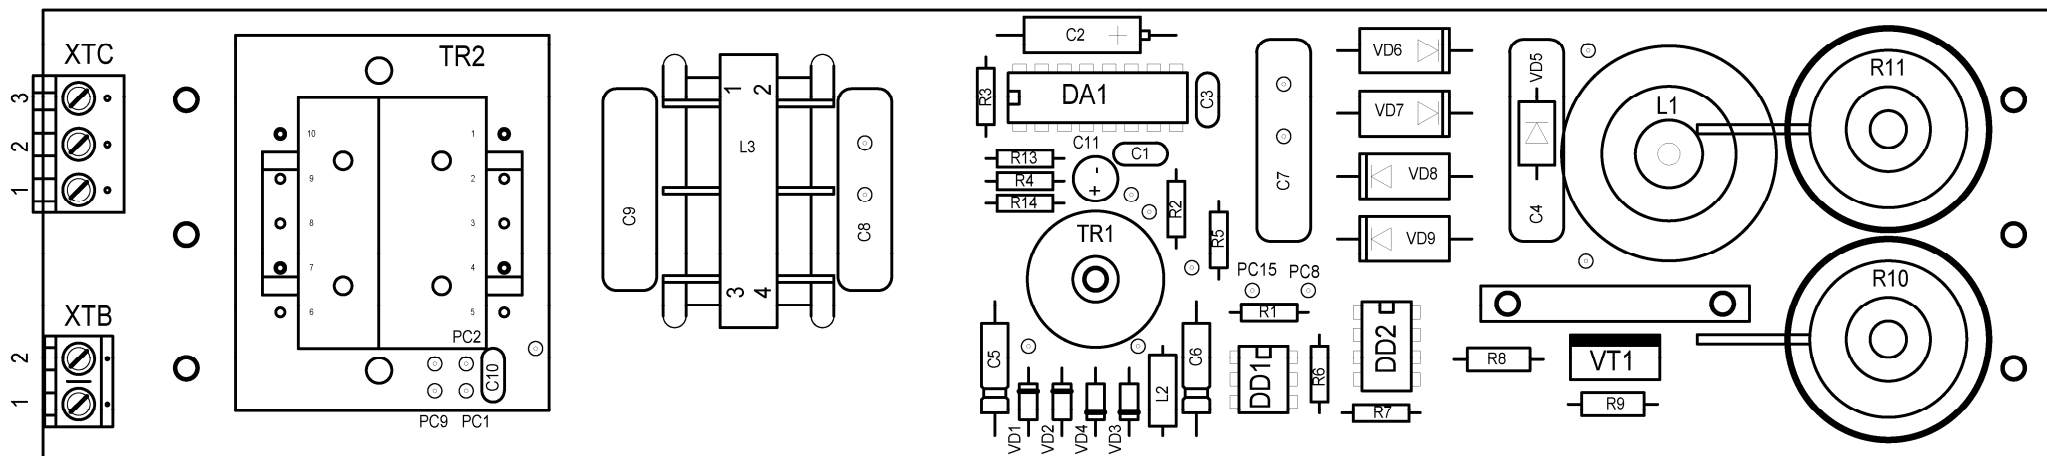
Блок регулятора тока накала ТВ03. Схема расположения элементов.
